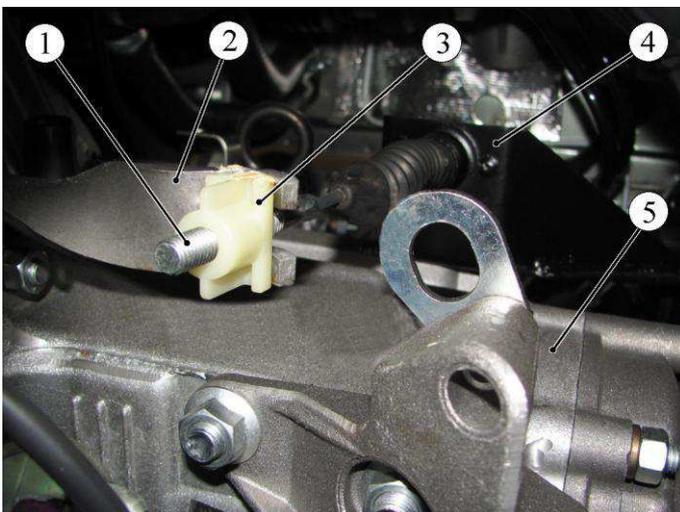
Отсоединение троса привода сцепления от коробки передач:
